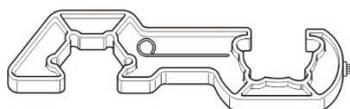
Dispositivo auxiliar para enroscar para desmontaje/montaje
